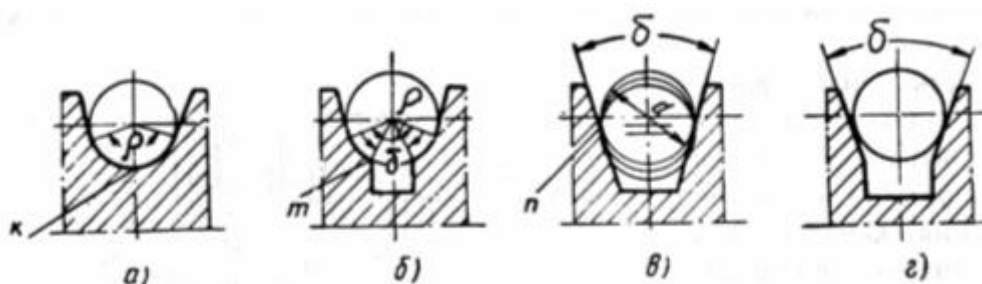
Профиль поперечного сечения канавки обода КВШ:
